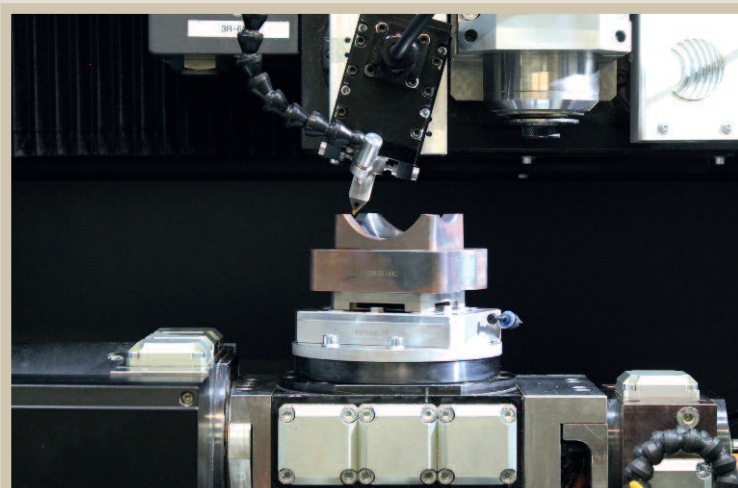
Formeinsatz auf Mikrobearbeitungsmaschine
